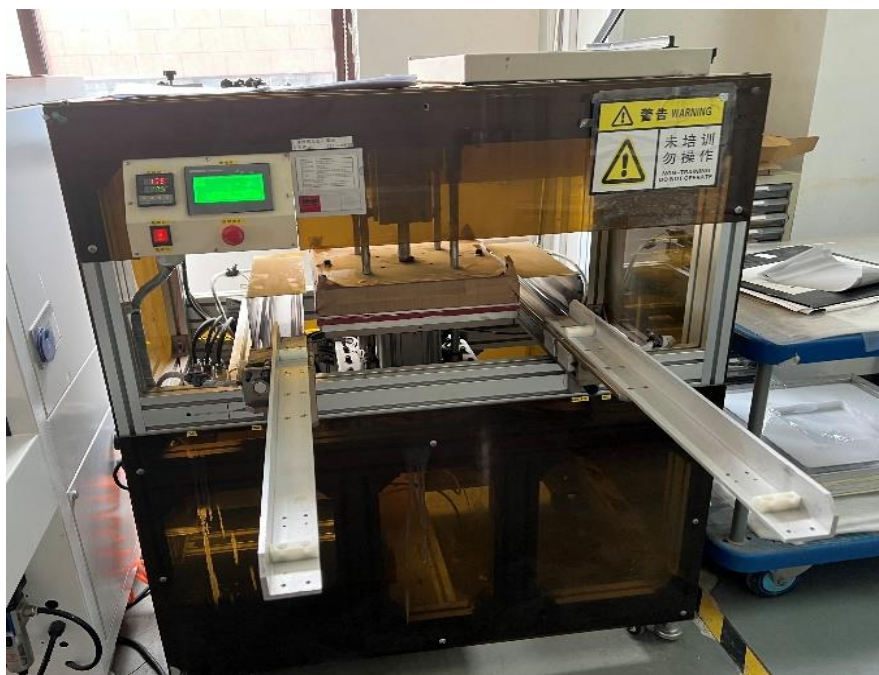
Umschweißanlage bei Frintrup NB SST
